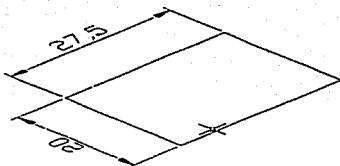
Vista frontal isométrica de la placa retensora.
